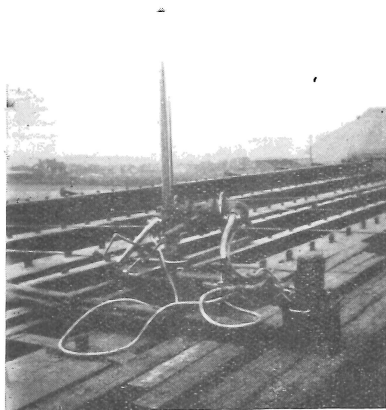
Ampoule à rayons X en station pour la radiographie d'une soudure horizontale.
